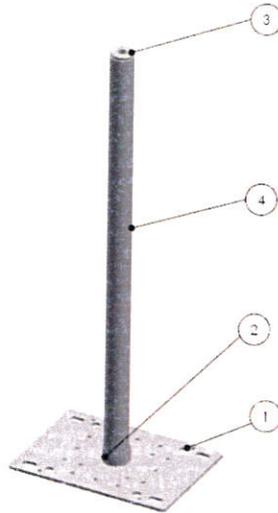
Anschlagseinrichtung, Typ: ESL 300-800 B / B-S / H / HD-B / S / S-KP / T
